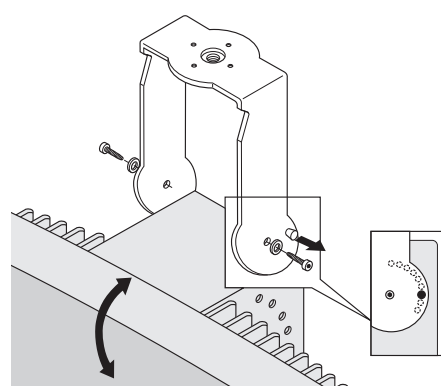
Fissaggio della staffa di montaggio al radiatore
